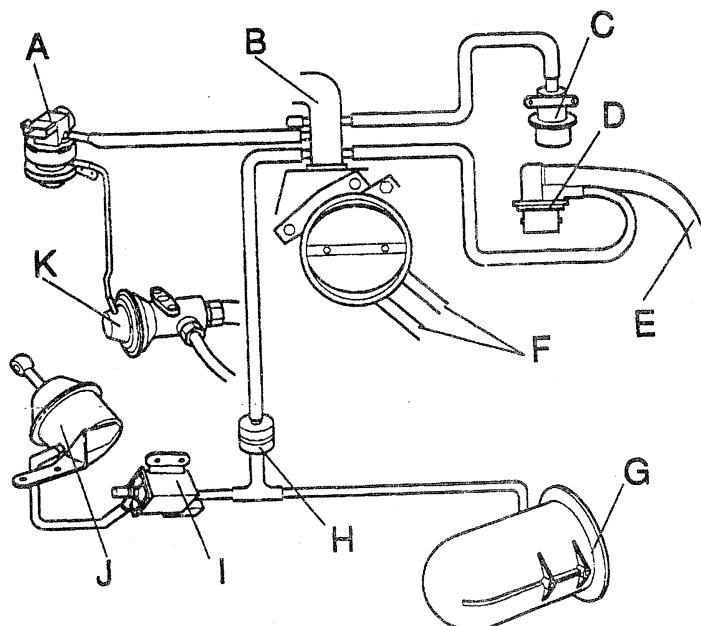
б. Проверка утечки воздуха (A — преобразователь EGR. B — соединения. C — регулятор давления топлива. D — управление вентиляцией картера. E — шланг маслouловителя. F — шланги системы EVAP. G — вакуумный бак. H — обратный клапан. i — магнитный клапан. j — вакуумный сервомеханизм. K — клапан EGR).
